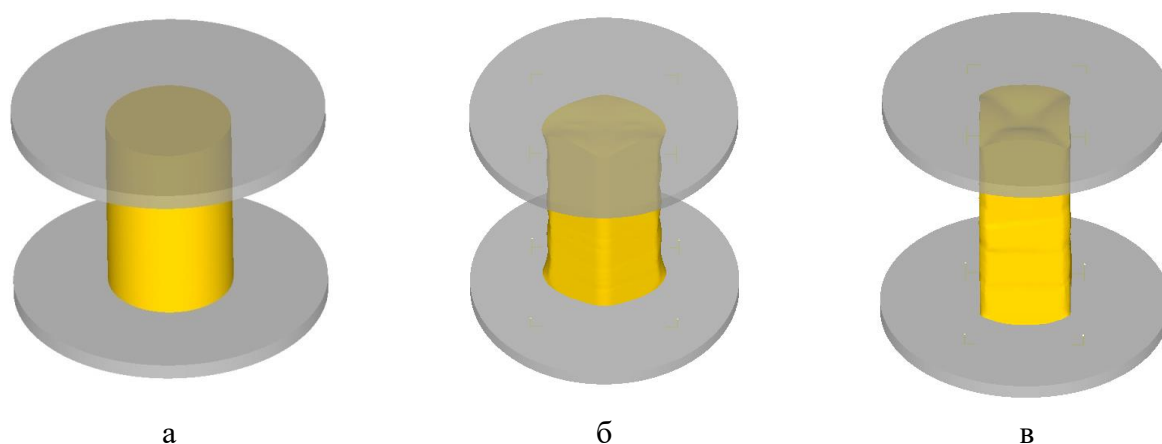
Схема осадки цилиндрической заготовки (а) и заготовки, профилированной на ромбовидное (б) и квадратное (в) поперечное сечение
